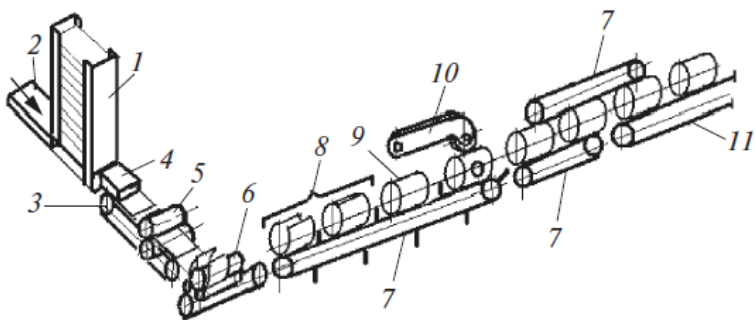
Схема автомата що виготовляє обичайки із зварним швом
